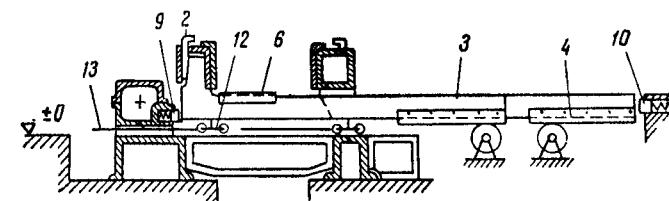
Схема манипулятора станка с односторонним расположением привода:
